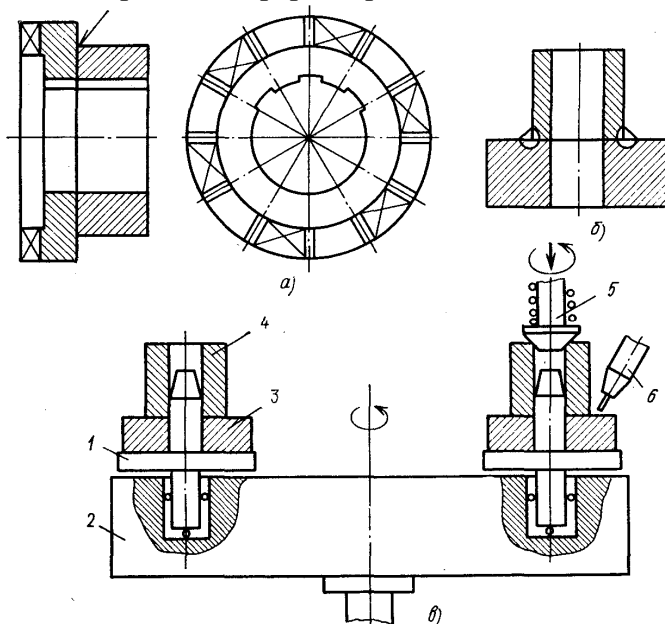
Автоматическая сборка и сварка двух заготовок:
